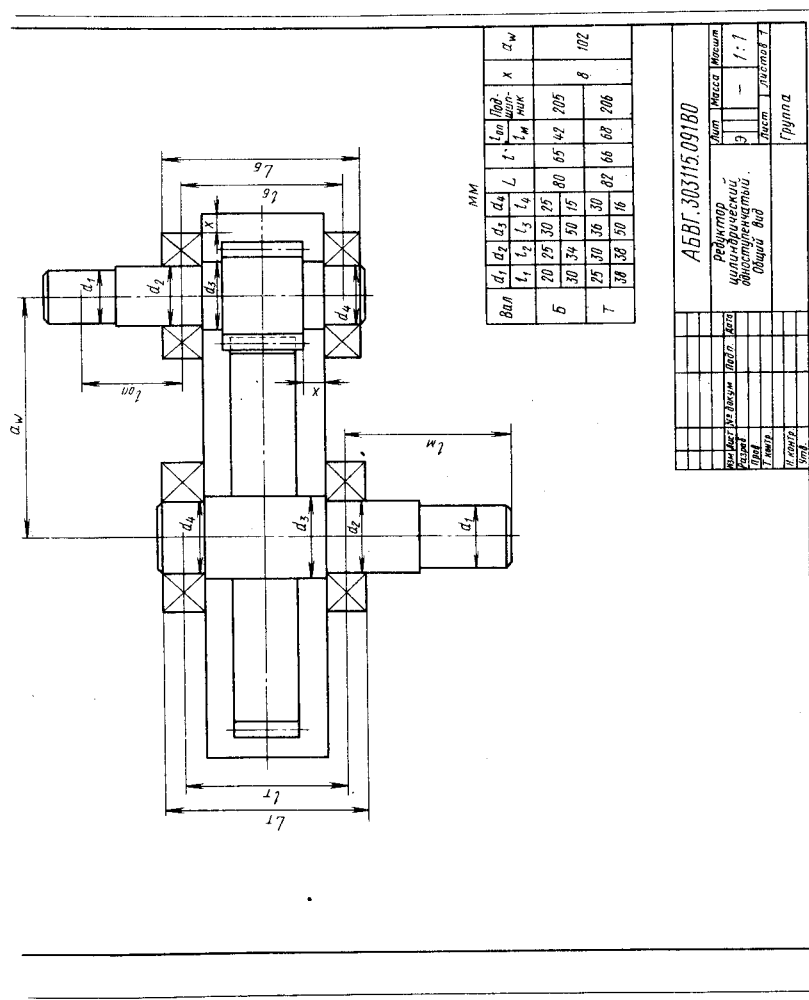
Пример эскизной компоновки цилиндрического одноступенчатого редуктора
